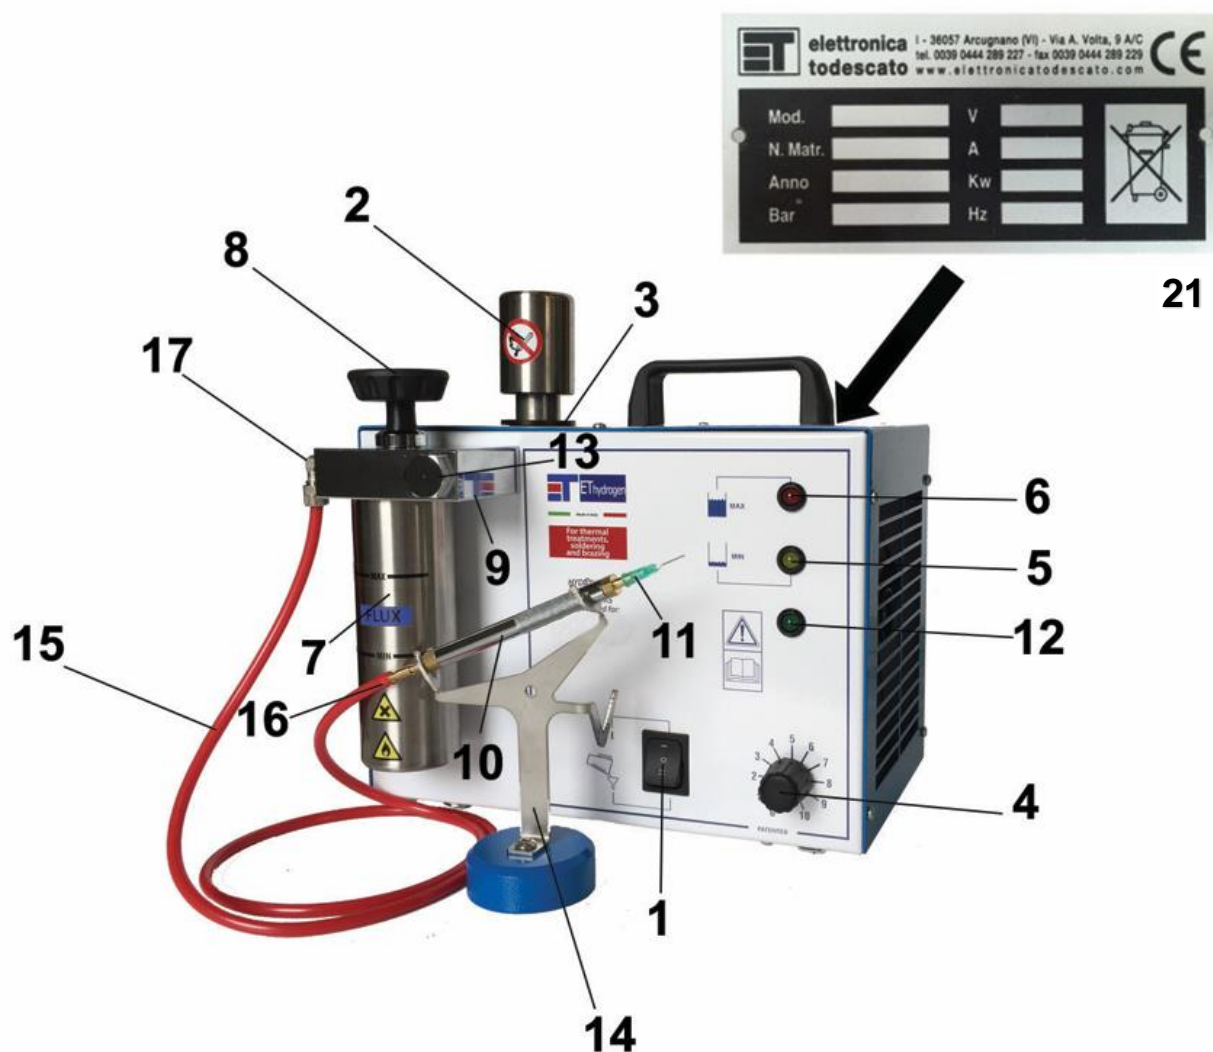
SALDATRICE E SUOI COMPONENTI
